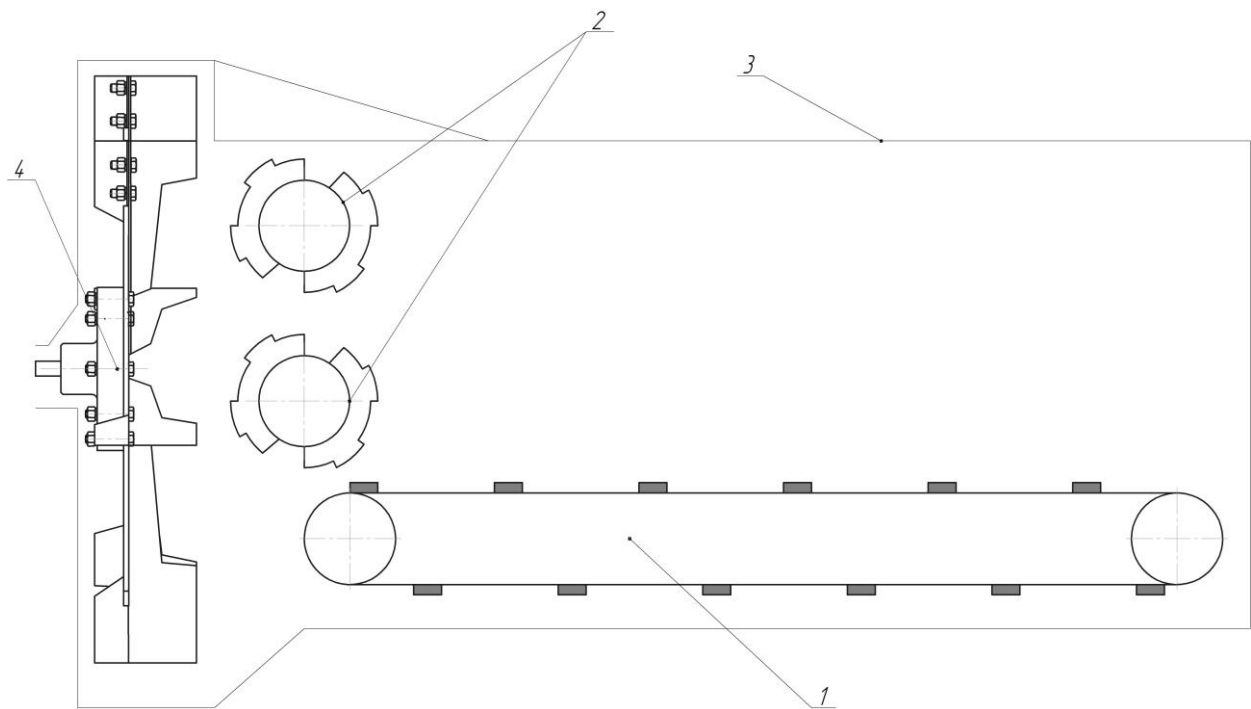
Схематична будова кормороздавача: 1 – подавальний механізм кузова; 2 – спрямовувально-вирівнювальний механізм; 3 – стінки кузова; 4 – дисково-лопатевий дозувальний механізм. [11, 12]
